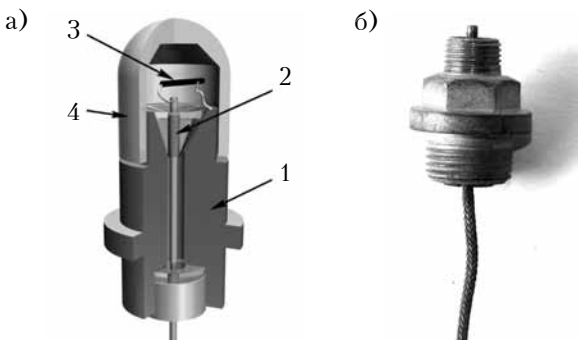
Конструкция (а) и внешний вид (б) датчика гидростатического давления: 1 — корпус; 2 — токовывод; 3 — чувствительный элемент; 4 — защитный колпачок
